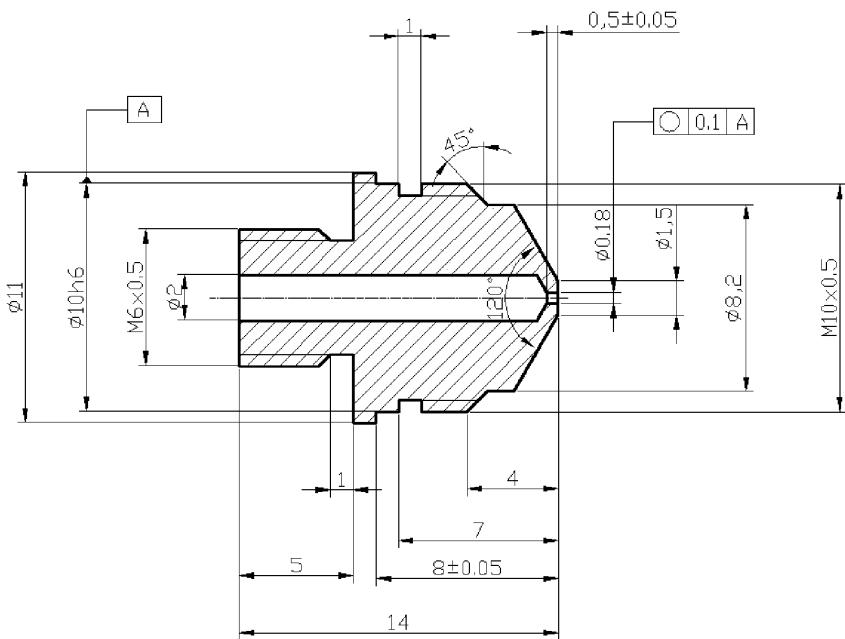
Горелка для зажигания образца (газовое сопло горелки)
